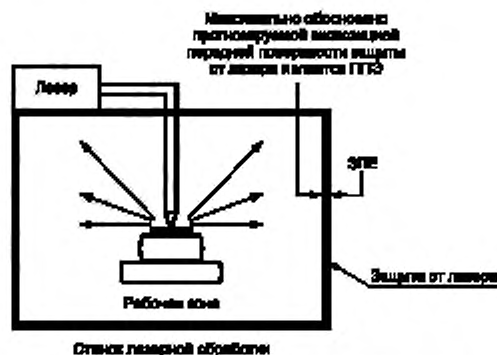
Пример защиты вокруг станка лазерной обработки
